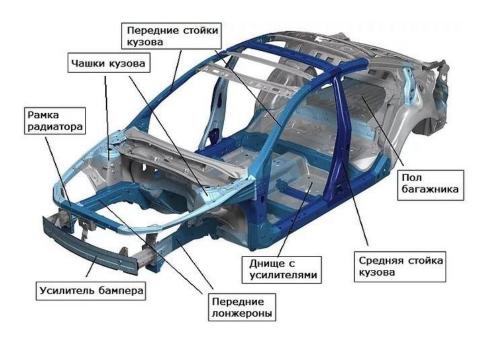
Перспективные направления применения лазерной сварки на автомобилях OAO «АВТОВАЗ»
